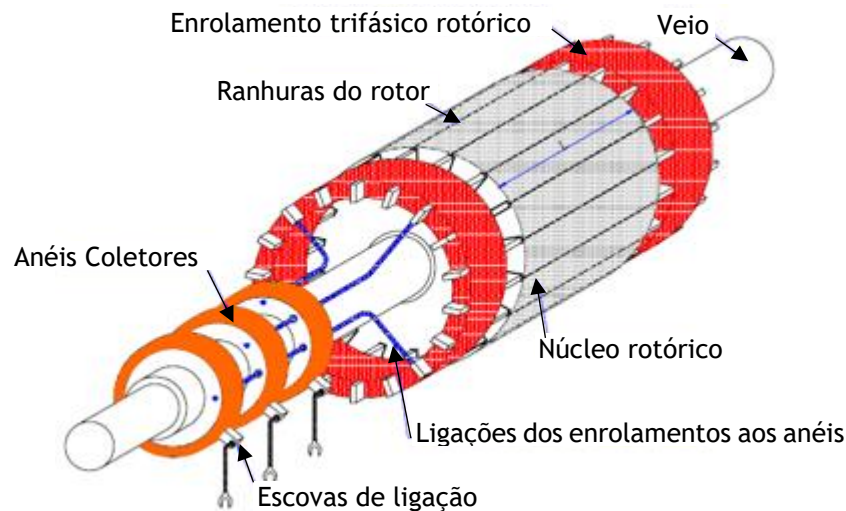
Exemplo esquemático de um rotor bobinado.
